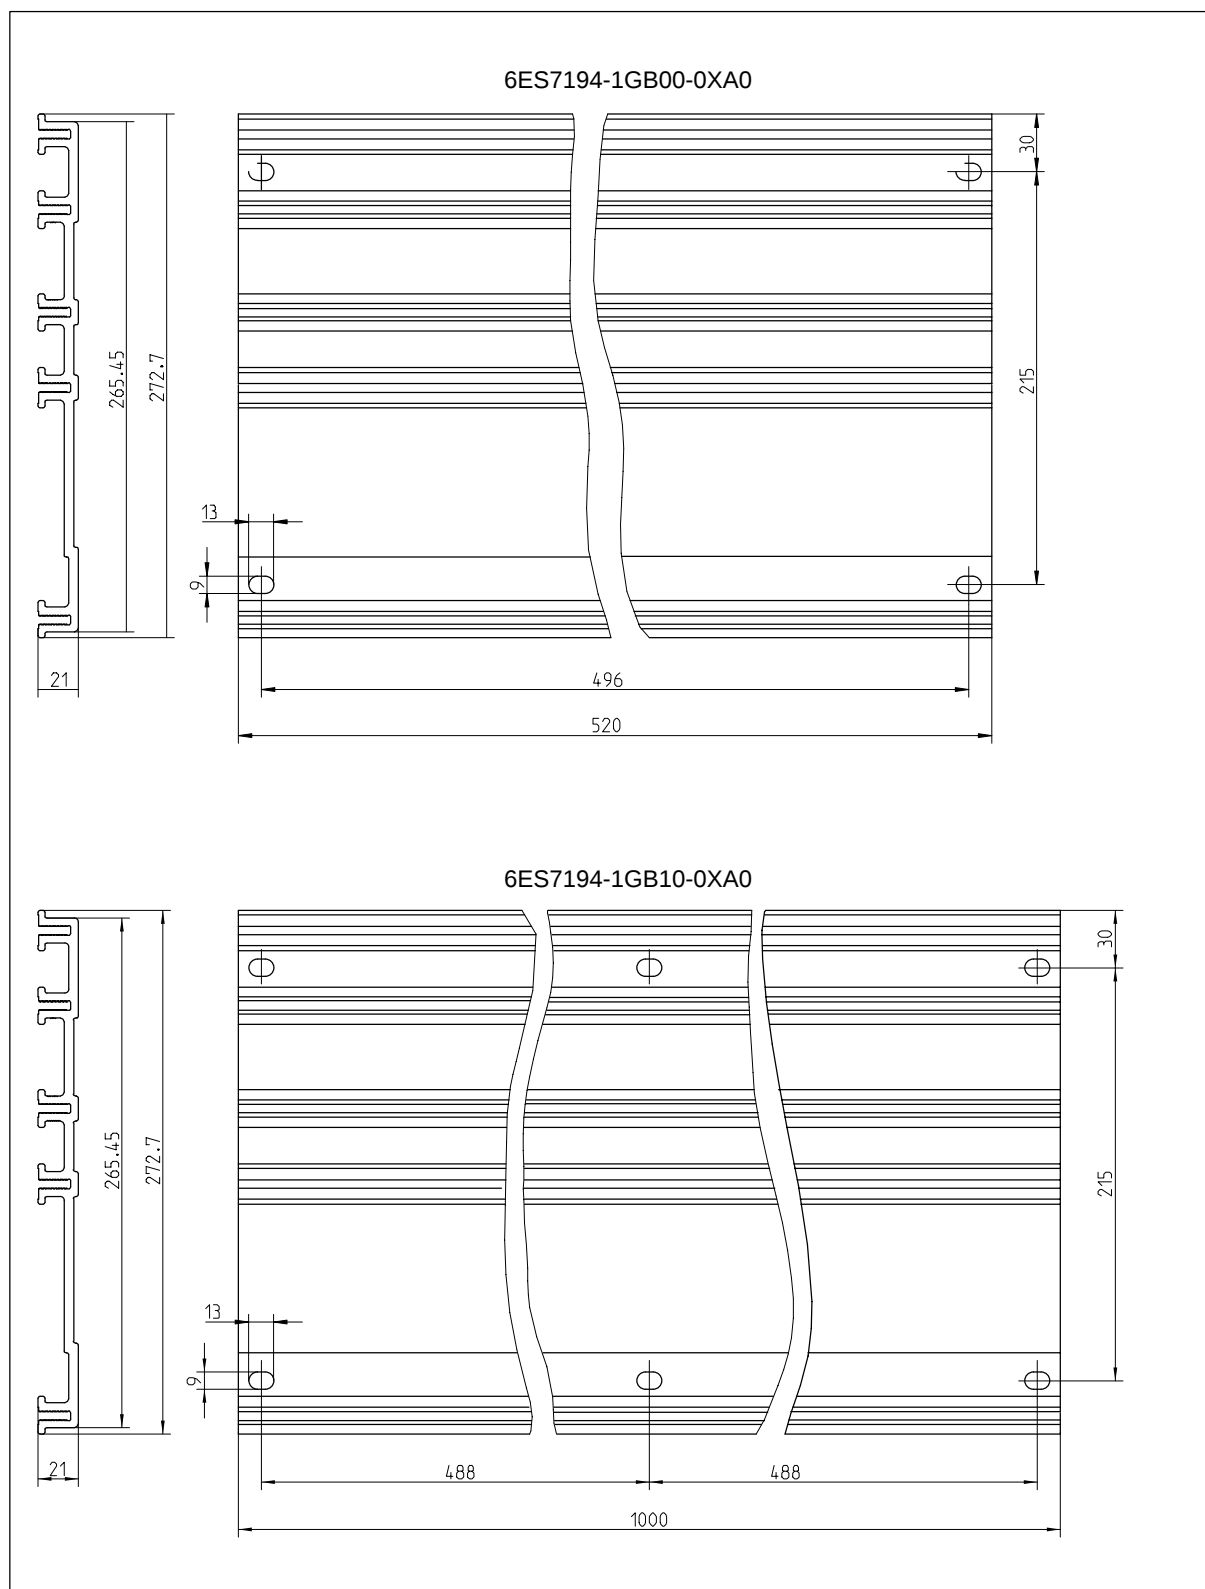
Croquis acotados de los perfiles soporte anchos
